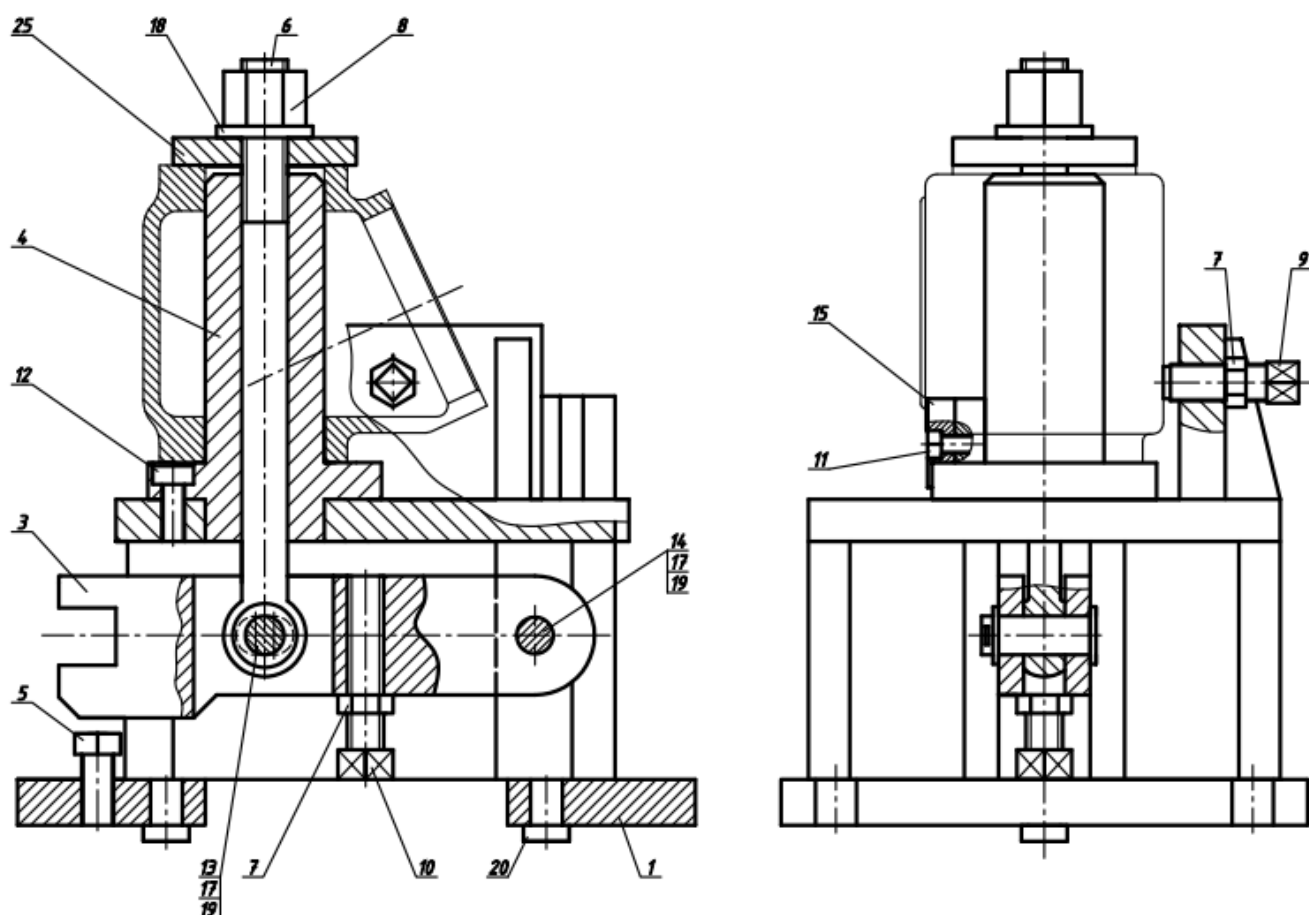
Пристрій для фрезерування деталі в розмір 53
